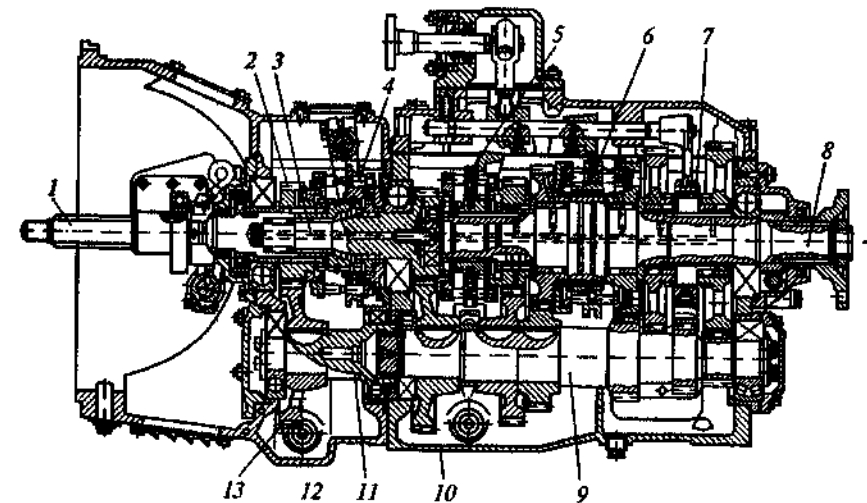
Коробка передач грузового автомобиля КамАЗ: 1 — ведущий вал; 2 и 13 — шестерни; 3 — первичный вал; 4... 6 — синхронизаторы; 7 — муфта; 8 — вторичный вал; 9 и 11 — промежуточные валы; 10 и 12 — картеры
